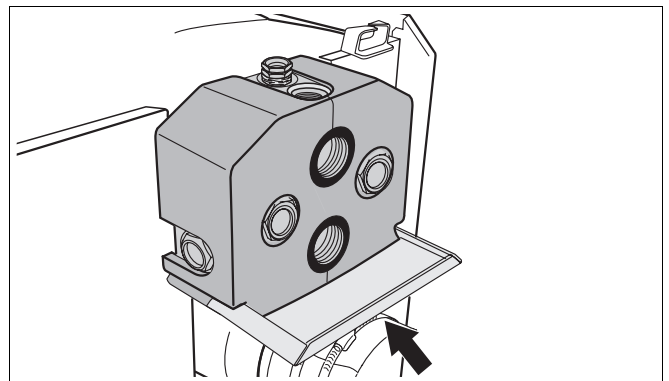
Montaggio della lamiera di protezione da irraggiamento
